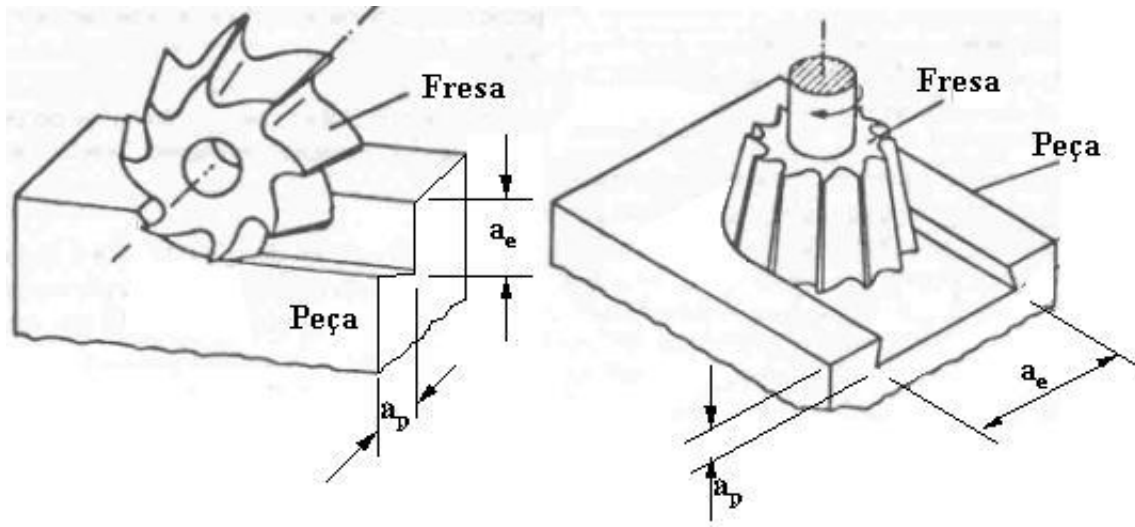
Exemplos de profundidade de usinagem e de penetração de trabalho.
